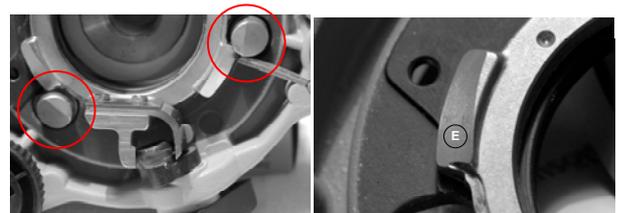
+b - Detailansicht (von unten) der Deckplatte mit gelöstem Vermessungsgerät (a); Detailansicht eines Klemmflanschs (b)
